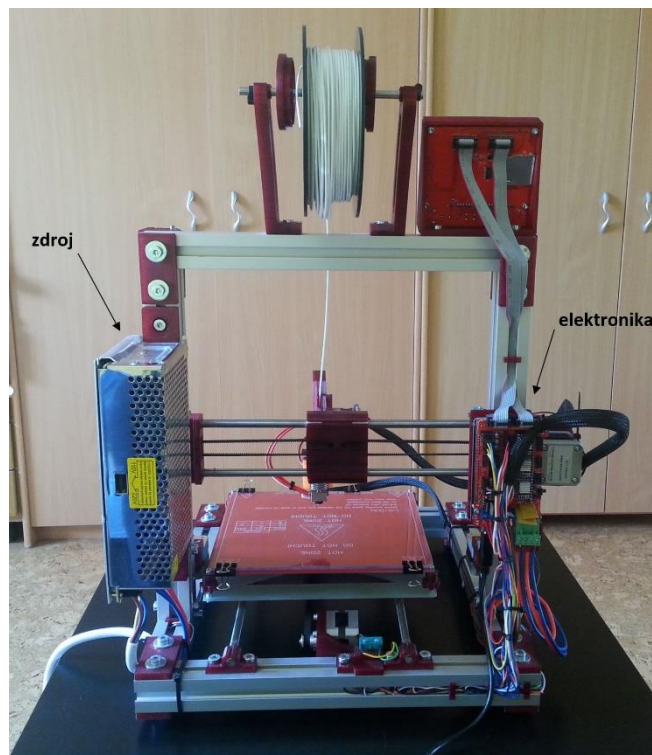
Zapojení elektroniky a úprava kabeláže.
